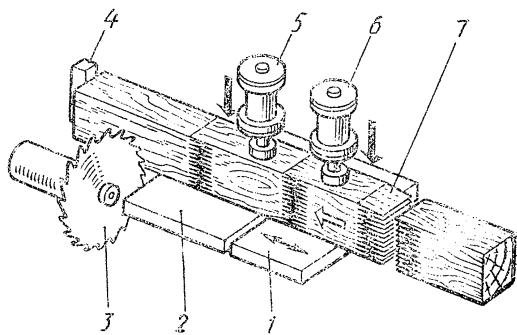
Схема пресса для склеивания прямолинейных заготовок на зубчатый шип:
